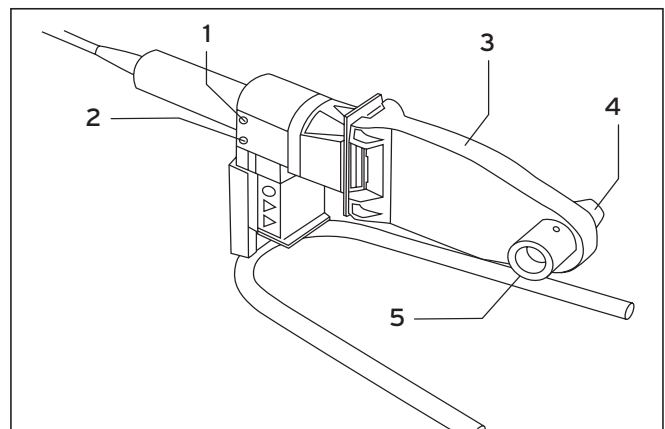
Benötigte Werkzeuge (2 von 2)
